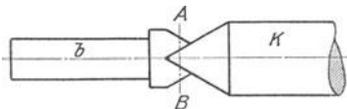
Kegelige Schraublehrenspitzen zur Messung des Flankenmaßes.
